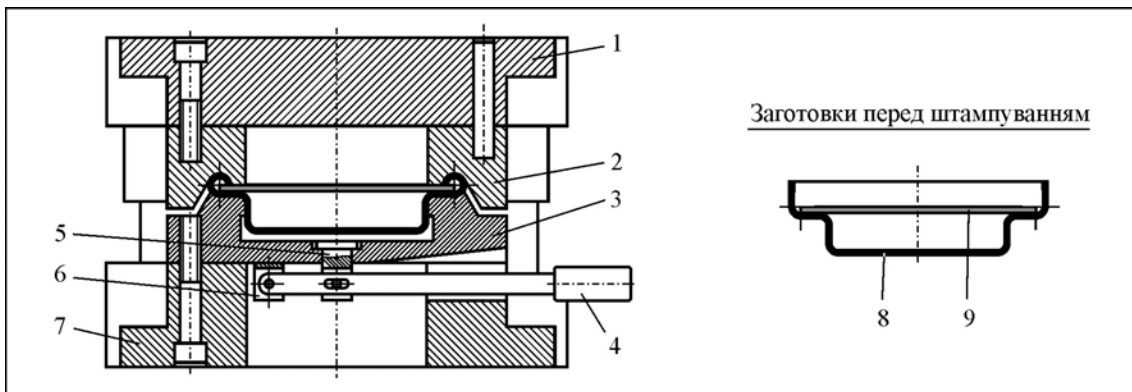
Штмп для складання двох деталей загортанням: 1 – верхня плита; 2 – матриця; 3 – пуансон; 4 – рукоятка; 5 – виштовхувач; 6 – кронштейн; 7 – нижня плита; 8 – сміть; 9 – диск
